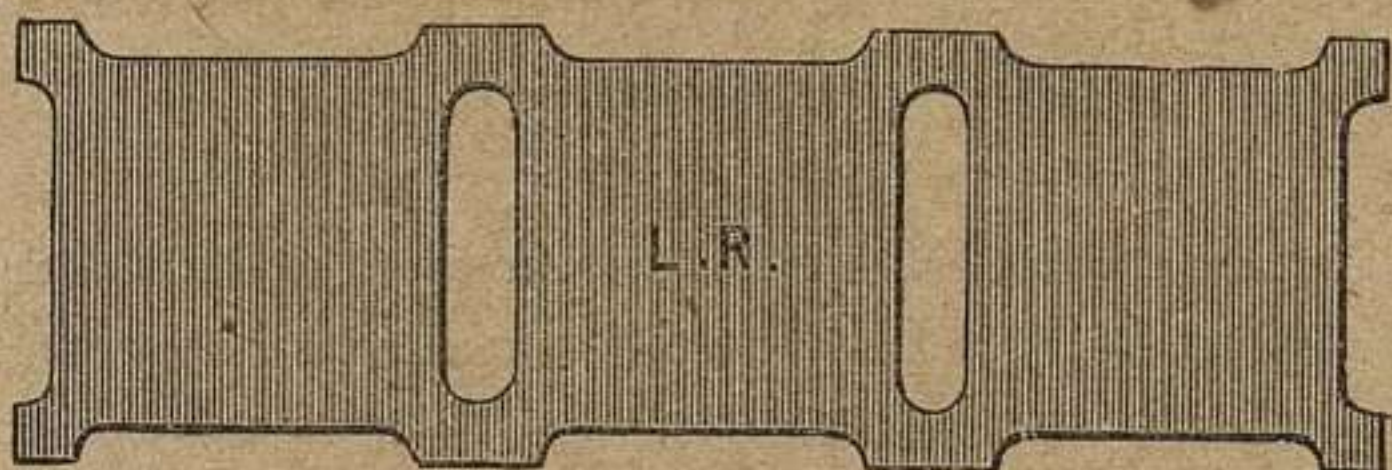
Separador triple de hoja de lata para tres secciones á la vez.
